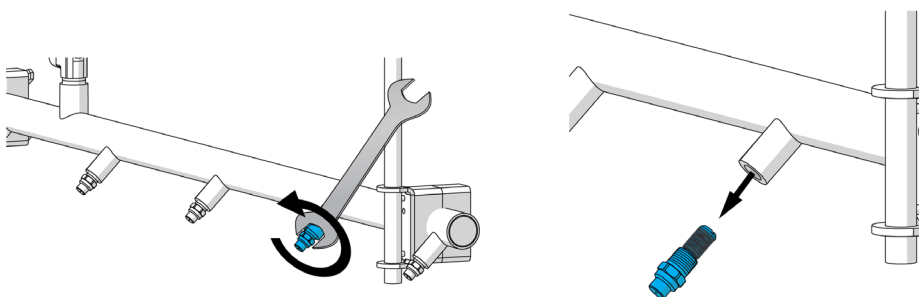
Extracción de la boquilla de la tubería de lavado de calles
